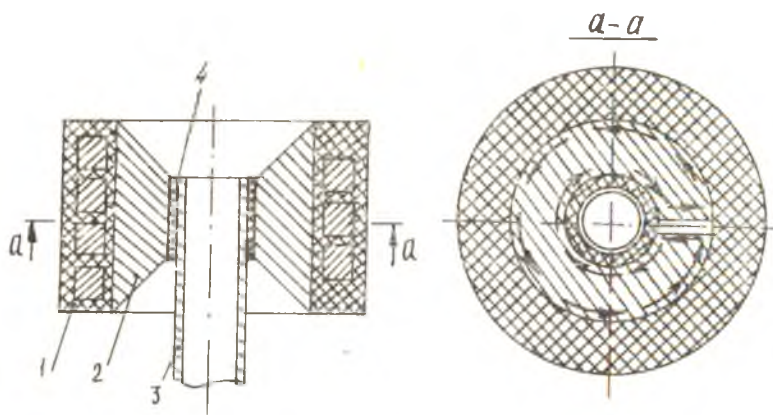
Схема индуктора с концентратором на обжим: 1—индуктор, 2—концентратор, 3—трубчатая заготовка, 4—изоляционная втулка
